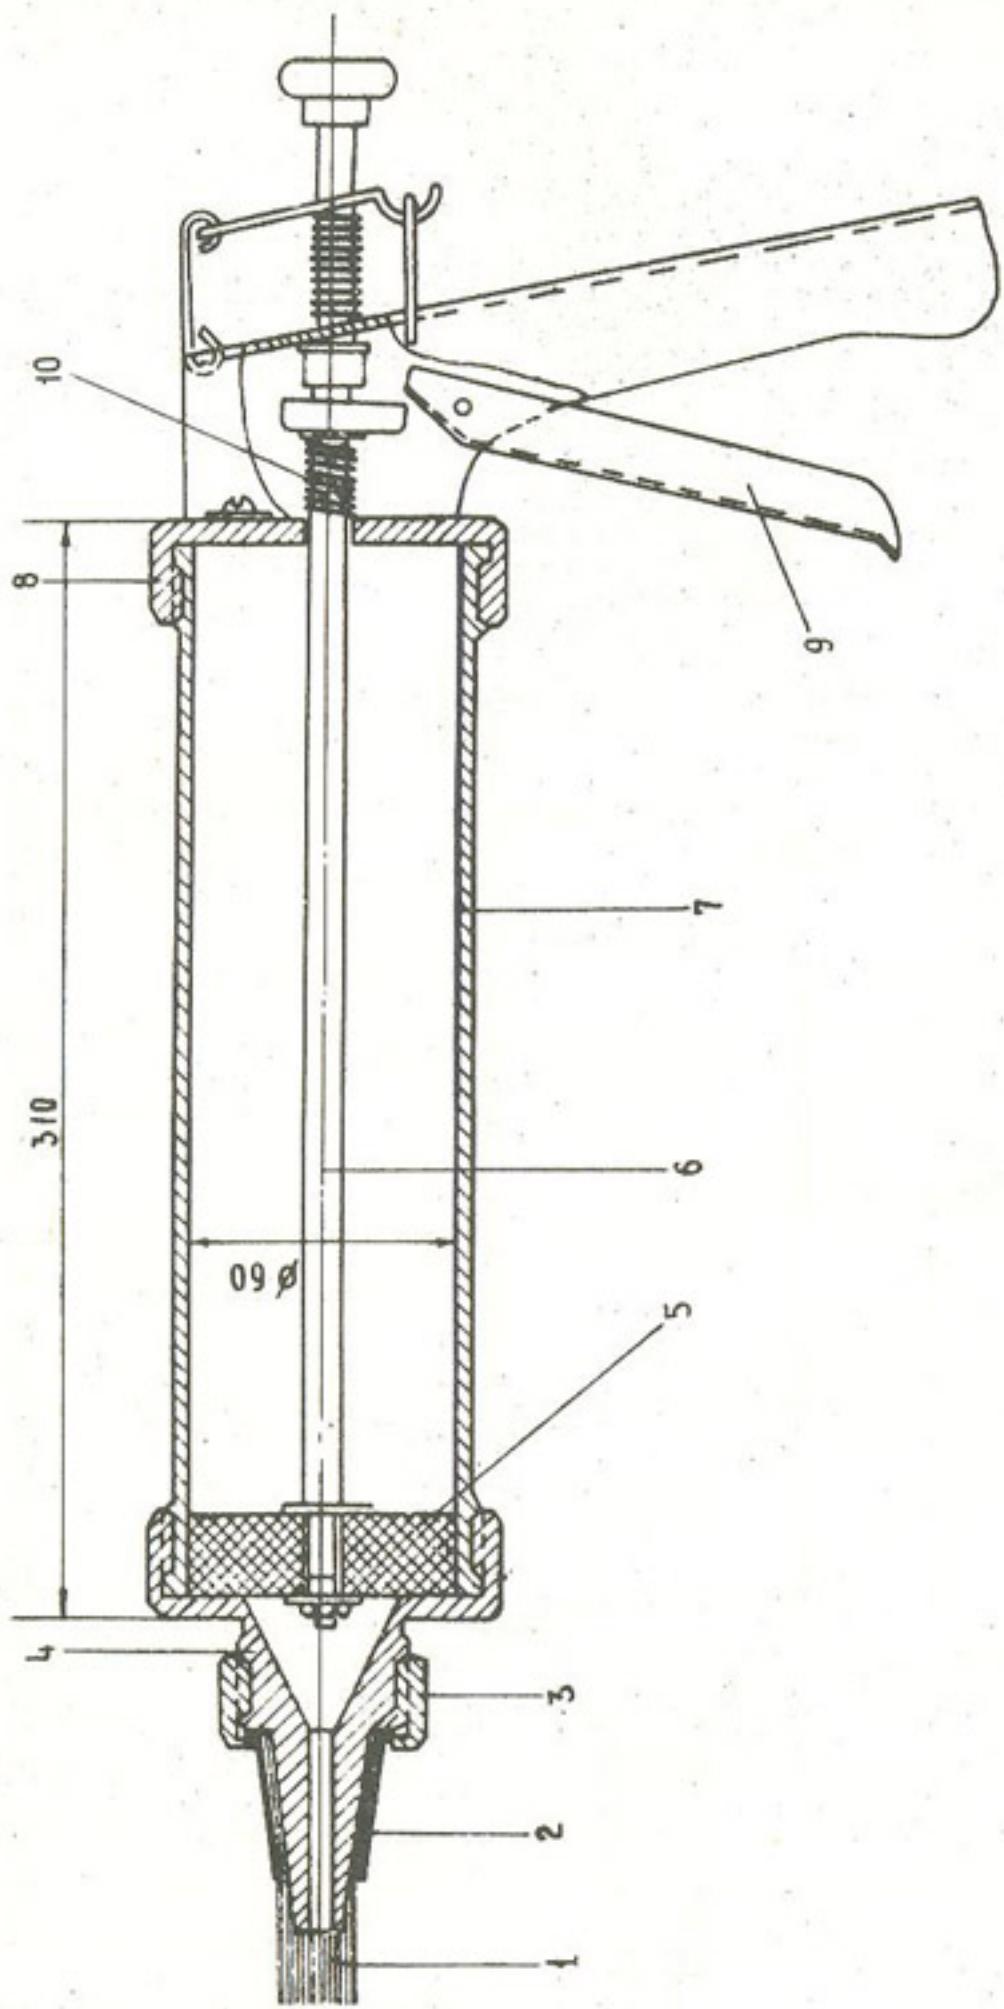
Ручной шприц для нанесения тиоколовых mastик: 1-лента mastика; 2-мундштук; 3-гайка; 4-наконечник; 5-поршень; 6-стержень; 7-цилиндр; 8-крышка; 9-ручка; 10-пружина
